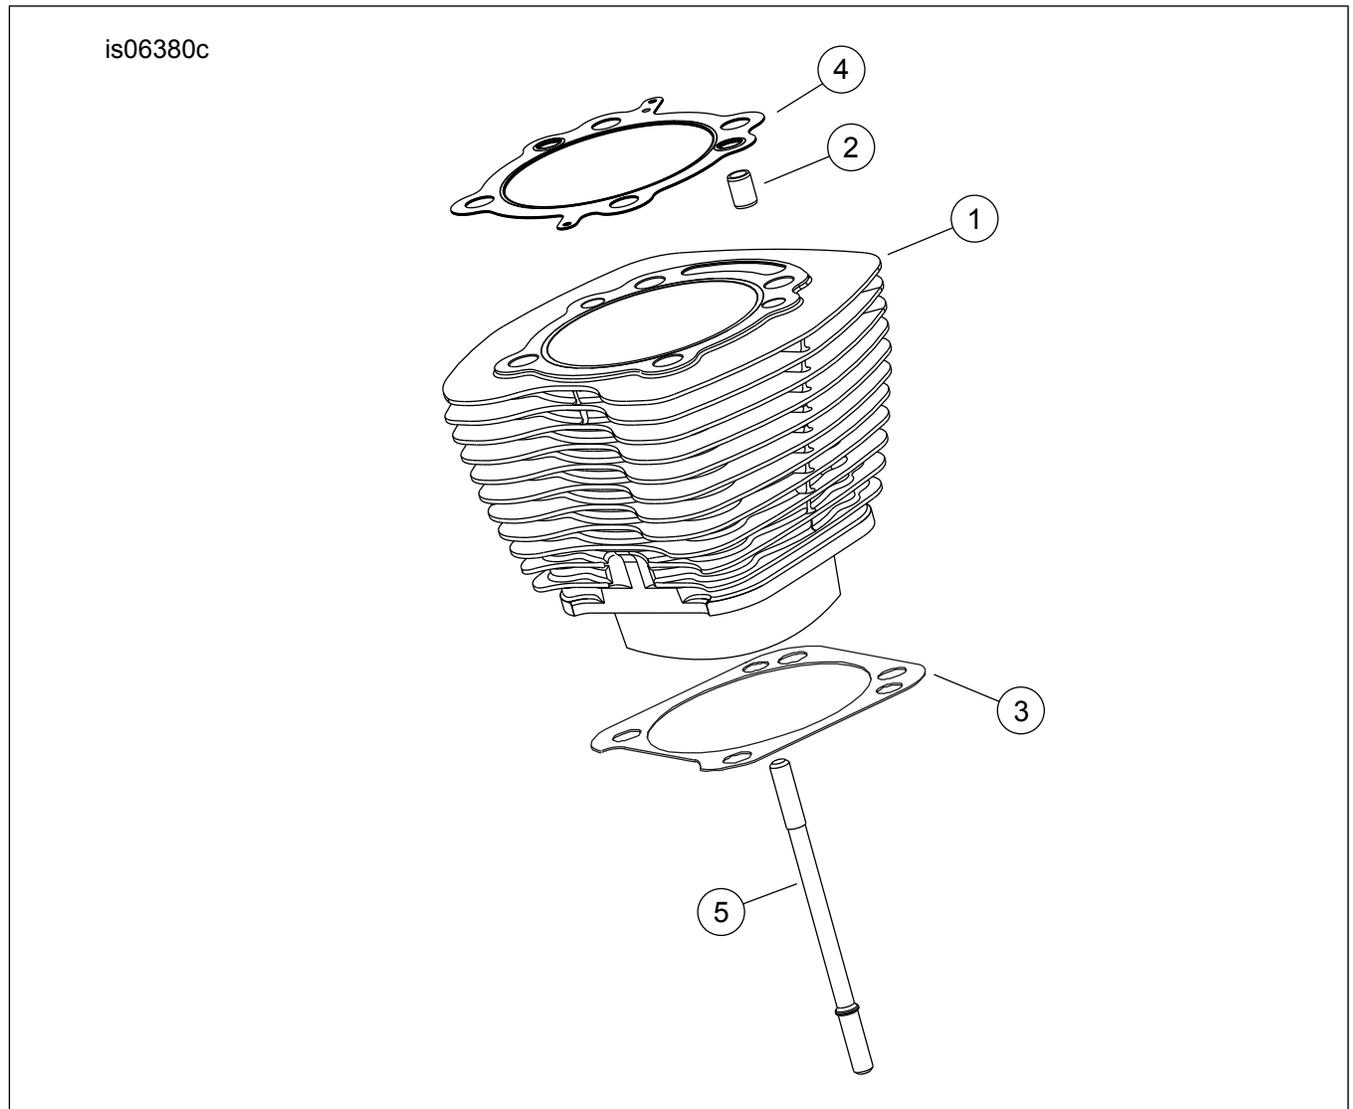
Cilindros del motor ensamblado Screamin' Eagle Pro SE120R (Beta)
